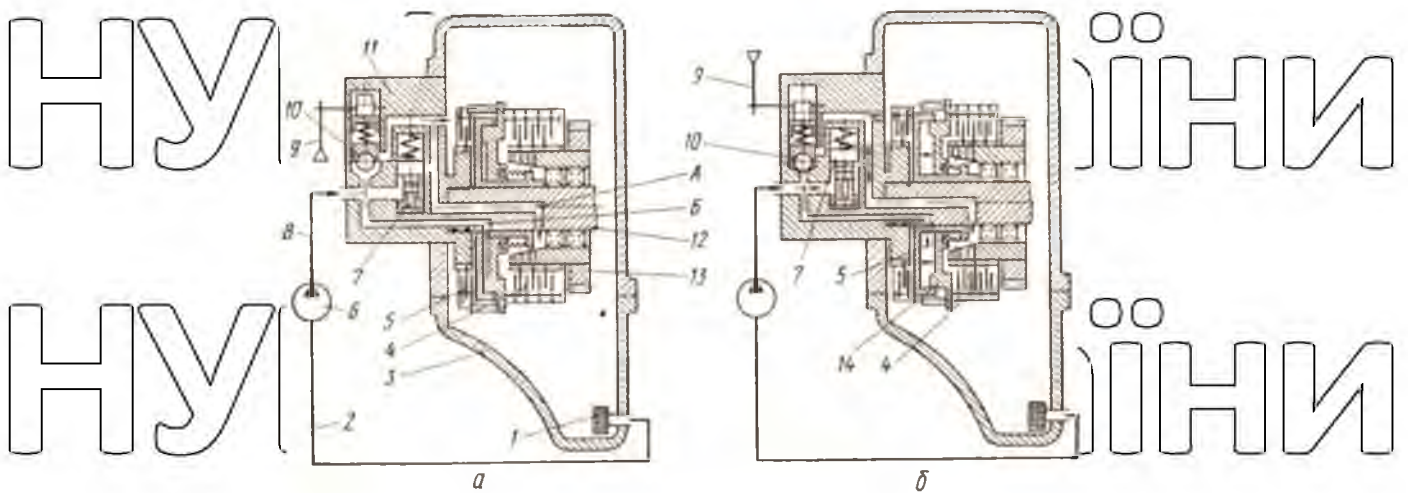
Схема гідросистеми редуктора валу відбору потужності:
